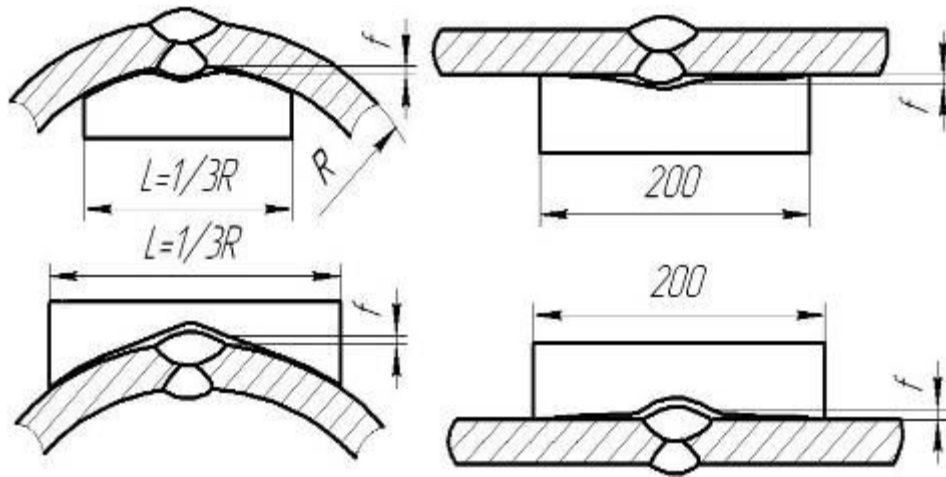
Шаблоны для проверки угловатости сварных швов
